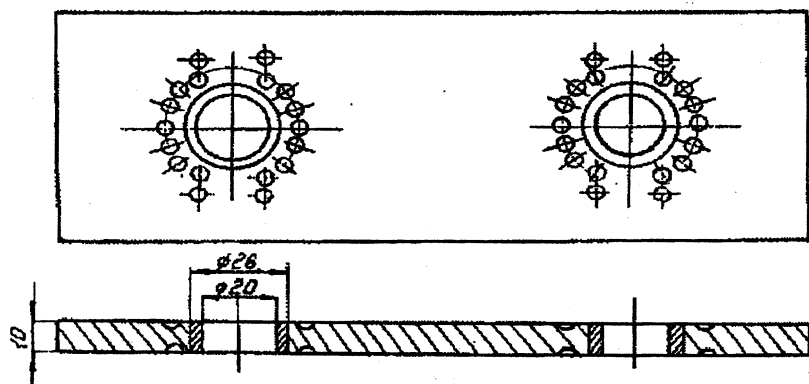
Образец с запрессованными втулками для испытаний на фреттинг усталость
